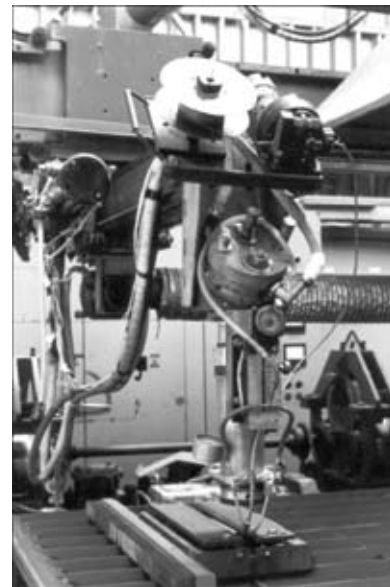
Общий вид фрагмента двухкоординатного манипулятора со сварочной головкой и механизмом подачи присадочной проволоки
